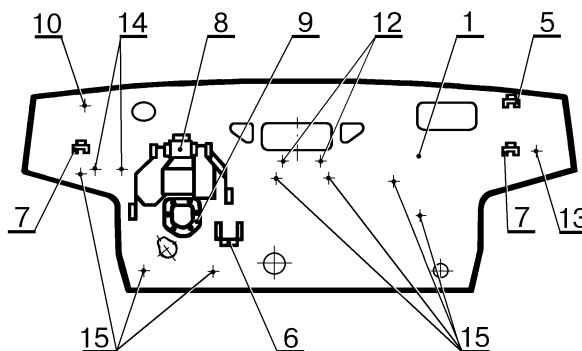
Детали щитка передка в сборе. Номера и наименования деталей, количество и шаг сварочных точек приведены в таблице 19 (всего 128±3 точки).
